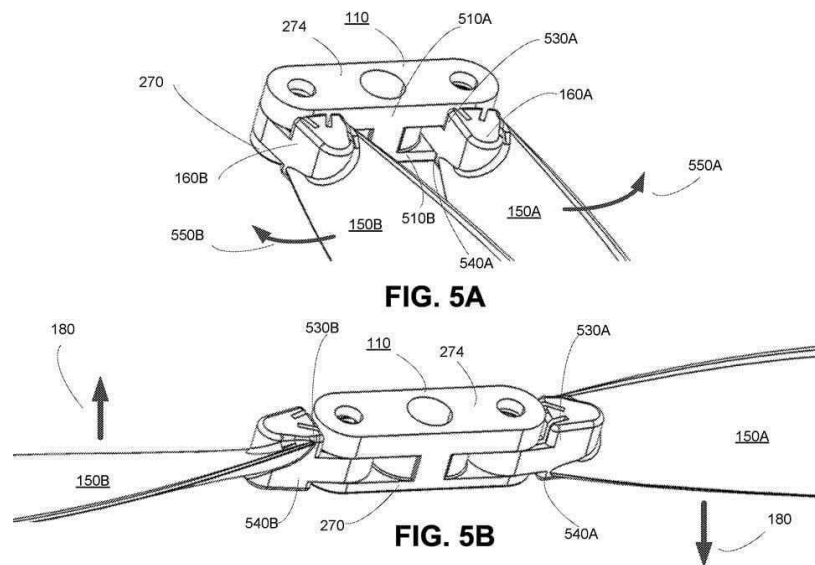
Fixace listů pomocí torzních pružin [6]
